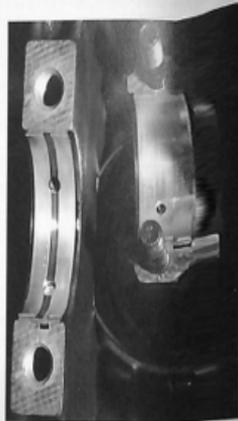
Cojinetes de apoyo de cigüeñal (izquierda y derecha).
